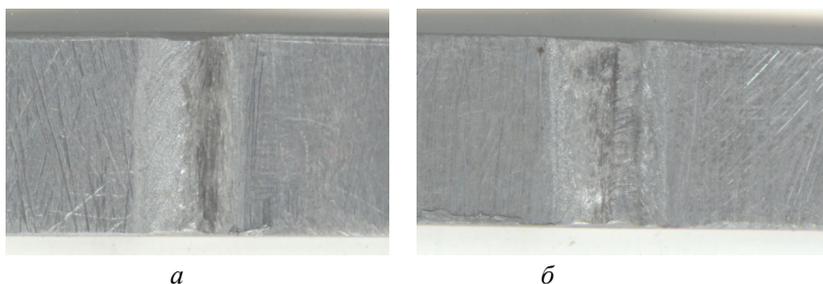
Внешний вид корня шва: *a* – образец 1; *б* – образец 2
